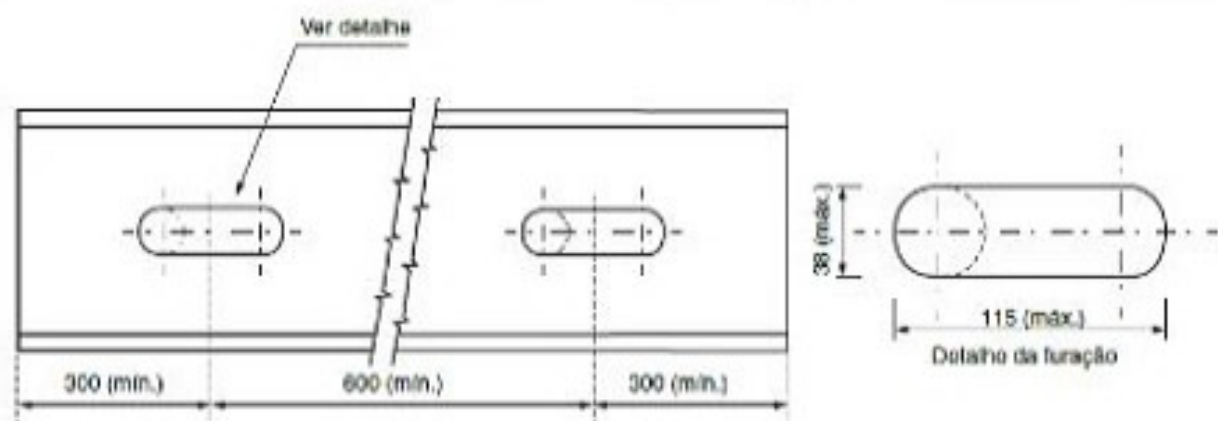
Detalhe de espaçamentos e furações nos perfis
